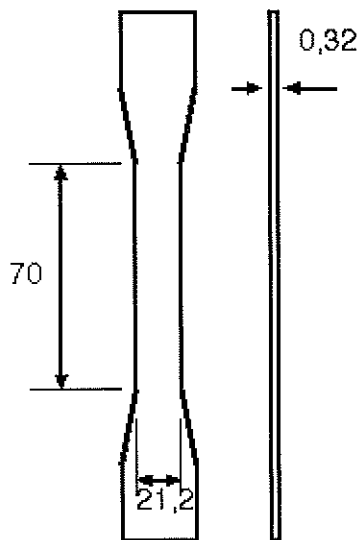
Geometria do corpo de prova ensaiado em tração (dimensões em mm)
